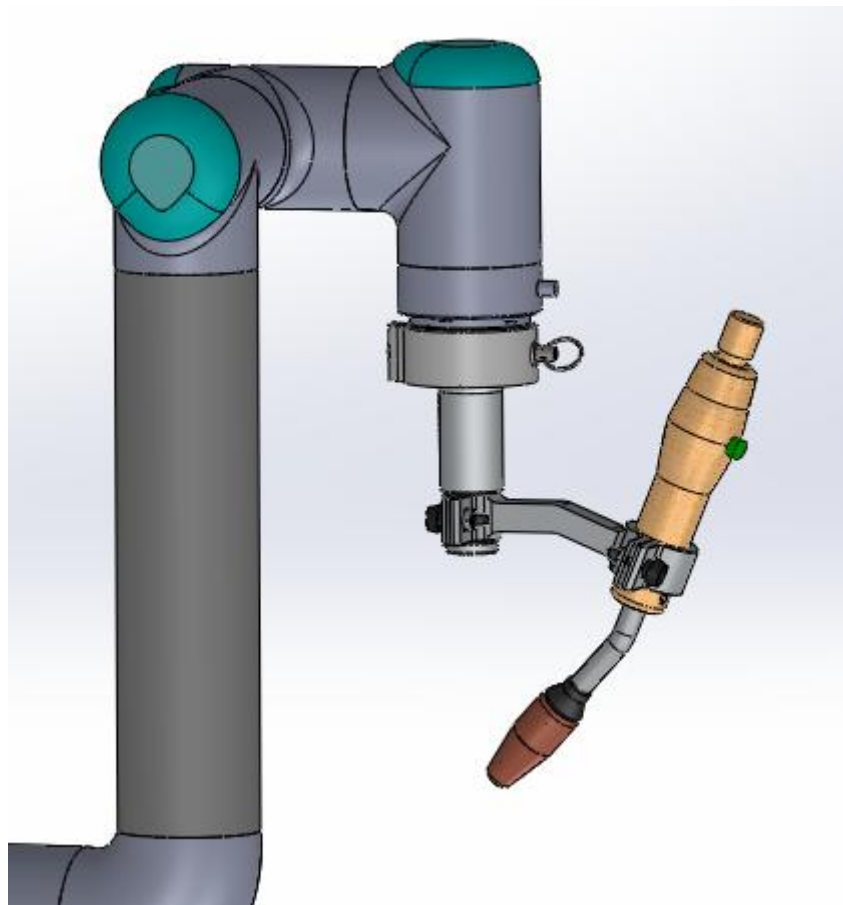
Robot Ur5 con herramienta de soldadura
